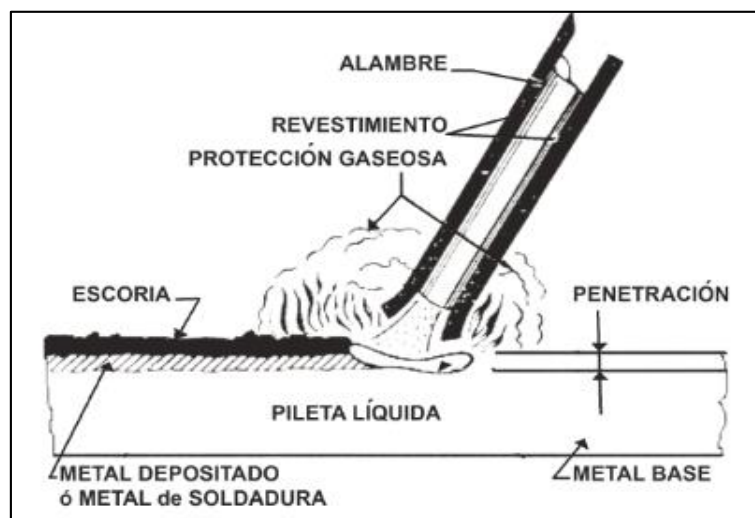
Proceso de soldadura por arco eléctrico protegido (SMAW)
